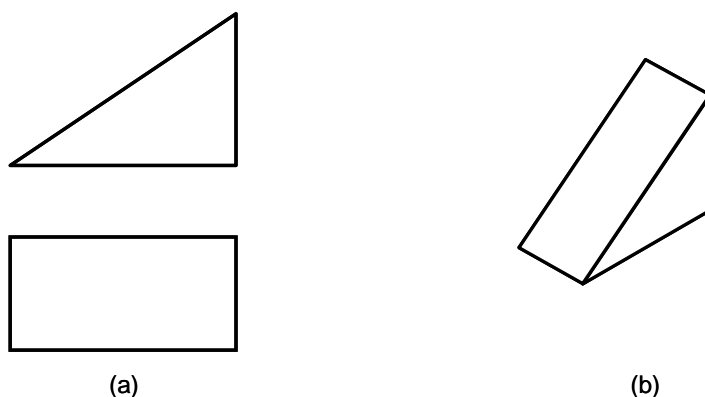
(a) Desenho técnico em multivistas; (b) Desenho técnico em isométrico.
